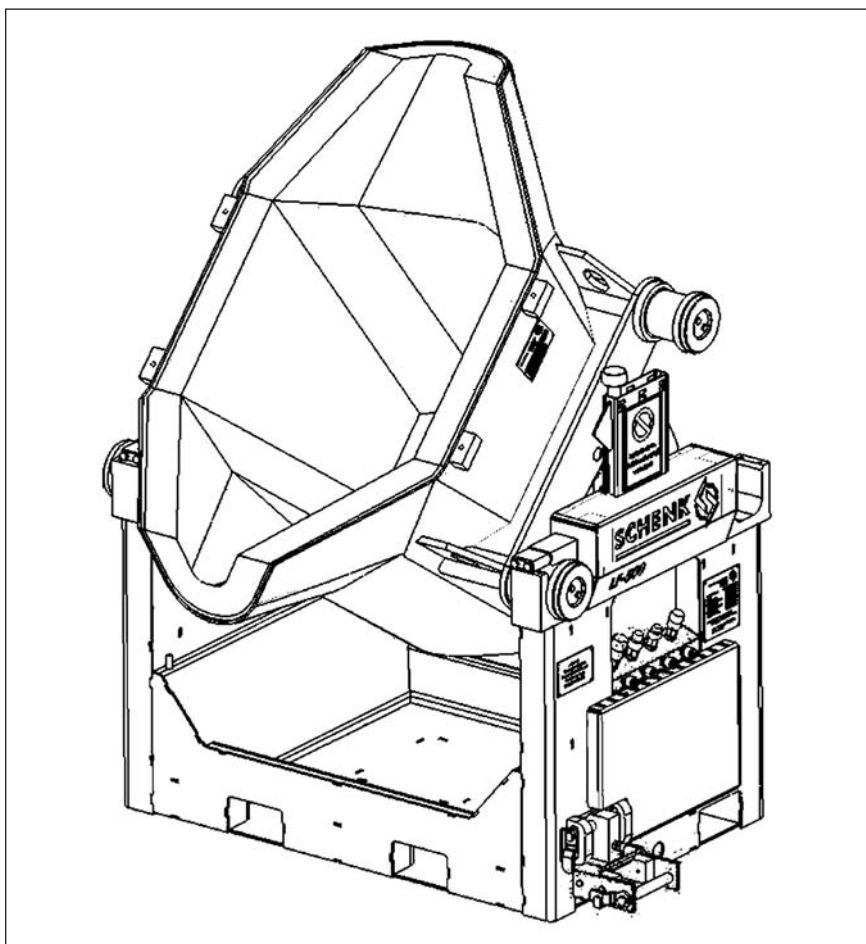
L-Модель навесного устройства, обеспечивающая гибкую работу автопогрузчиков с вилочными захватами
